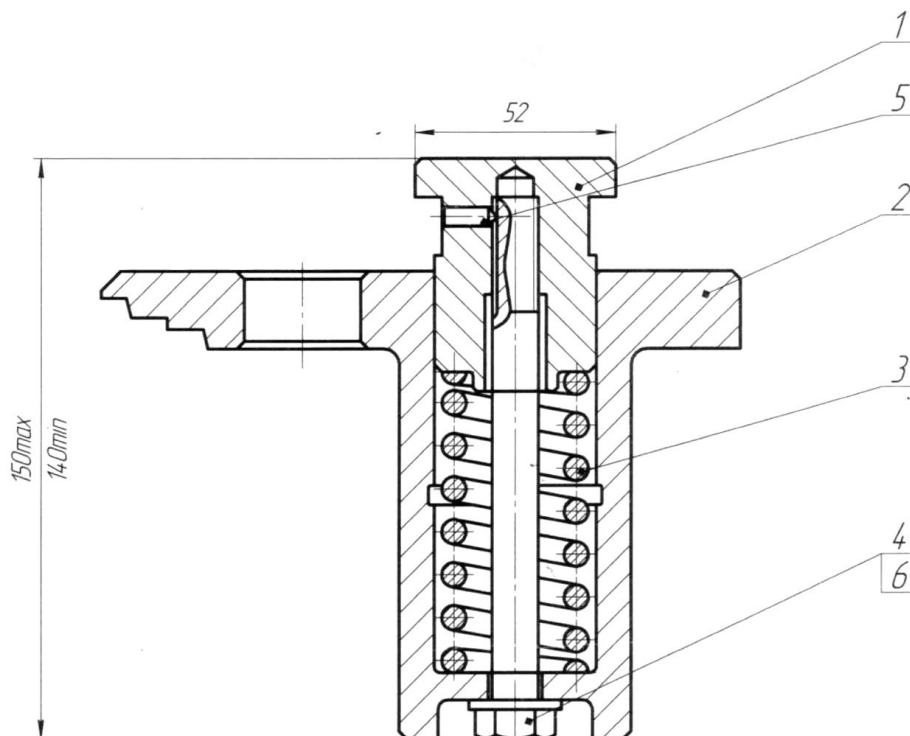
Наставка для запресовування зовнішніх обойм роликотішипників 7122 та 7224: 1 – хвостовик, 2 – упор, 3 – пружина. 4 – болт, 5 – фіксатор. Наставка дозволяє без перекосів запресовувати зовнішні обойми роликотішипників 7122 та 7224.
